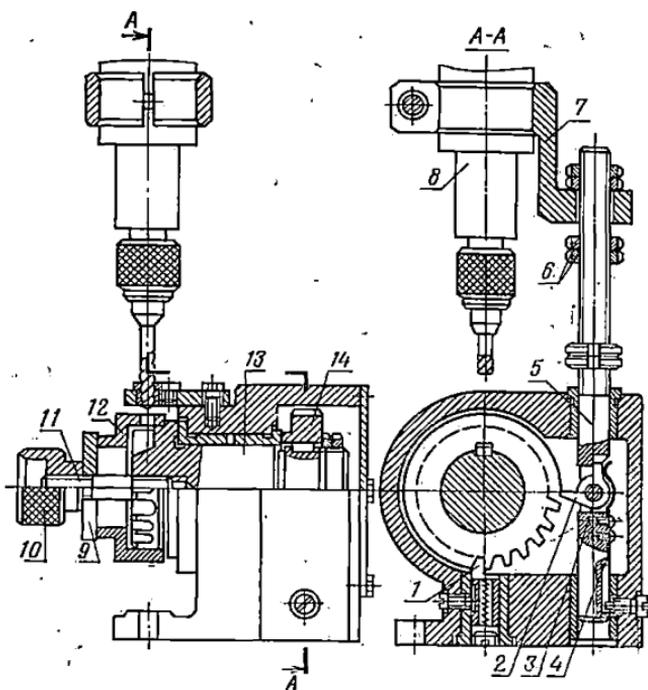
Поворотный кондуктор с автоматическим поворотом детали:
